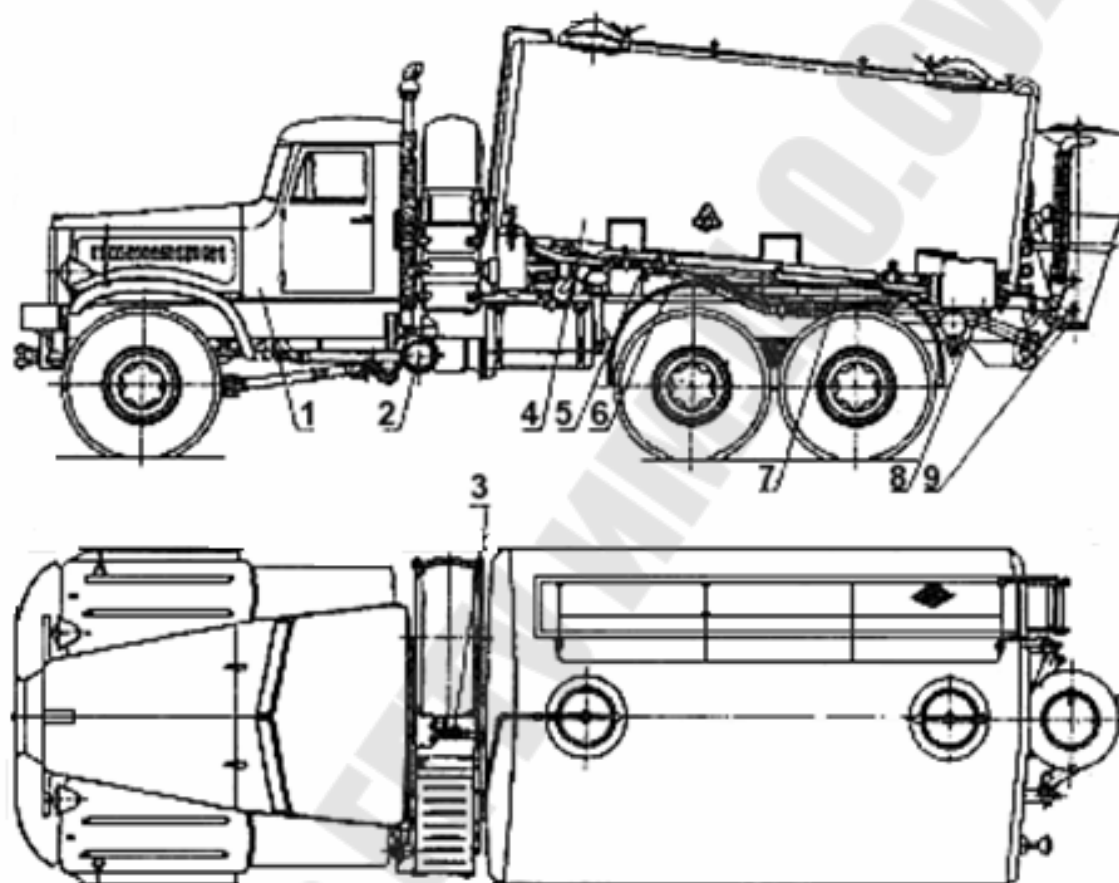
Конструкция цементировочного агрегата: 1 – шасси автомобиля; 2 – коробка отбора мощности; 3 – блок водоподающий с центробежным насосом; 4 – насос; 5 – колено шарнирное; 6 – колено шарнирное сдвоенное; 7 – бак мерный с донными клапанами; 8 – бачок цементный; 9 – манифольд
